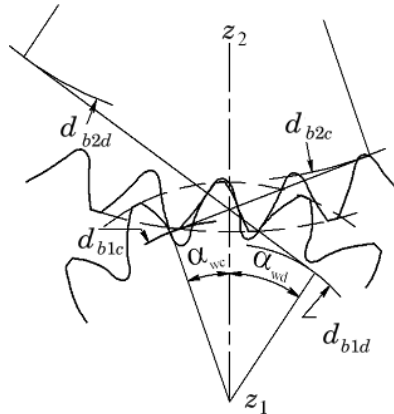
Схема зацепления зубьев шестерни и колеса с асимметричными зубьями [13]
